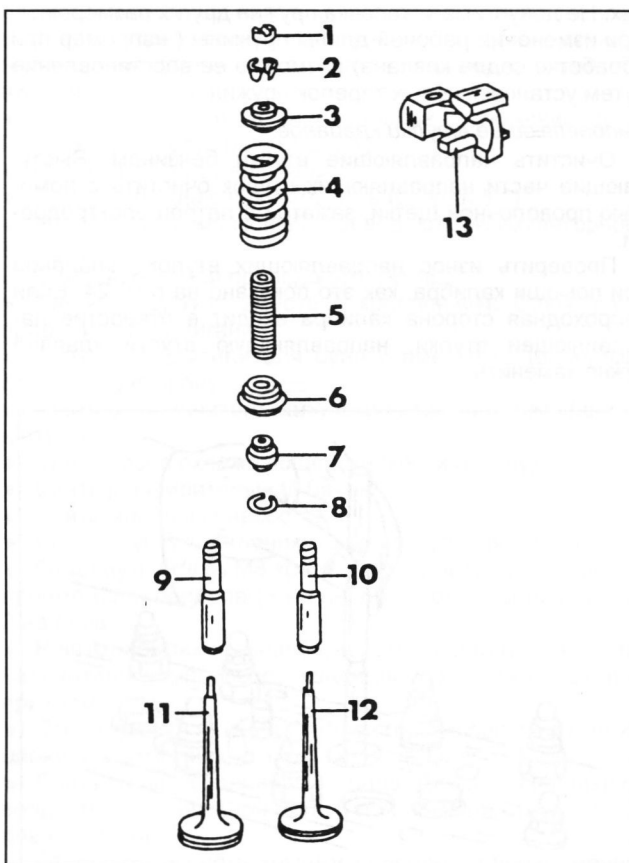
Клапанный механизм. 1 - толкатель, 2 - сухари, 3 - тарелка пружин, 4 - наружная пружина, 5 - внутренняя пружина, 6 - механизм поворота клапана, 7 - маслоотражательный колпачок, 8 - установочное кольцо, 9 - направляющая втулка впускного клапана, 10 - направляющая втулка выпускного клапана, 11 - впускной клапан, 12 - выпускной клапан, 13 - коромысло.
